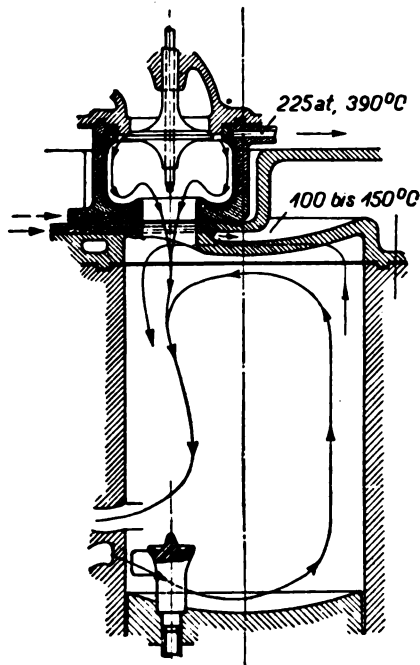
Zweitakt-Dieselmachine mit besonderem Brennraum und HD-Kühlung
